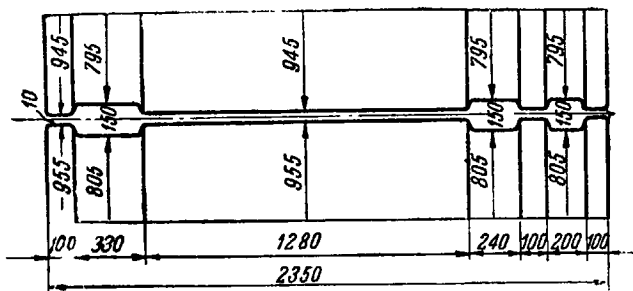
Калибровка валков блюминга со свободным уширением (гладкая часть бочки — посередине валка)
